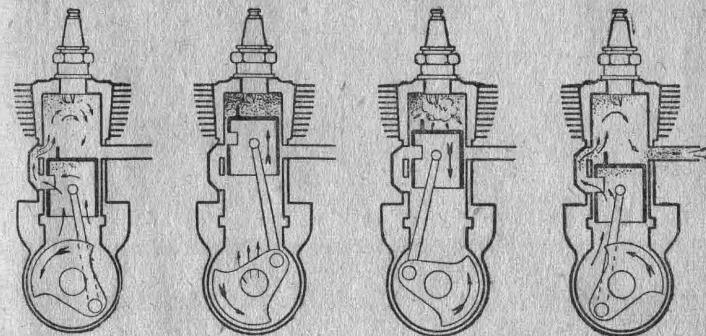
, 7, 8 и 9. Схемы работы двигателя.
